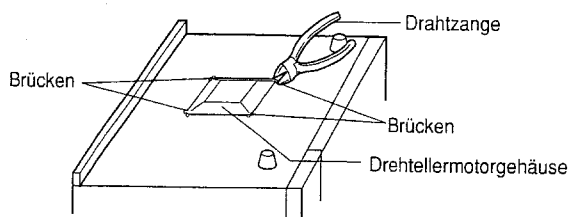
(a). Ausbau des Drehtellermotorgehäuses
